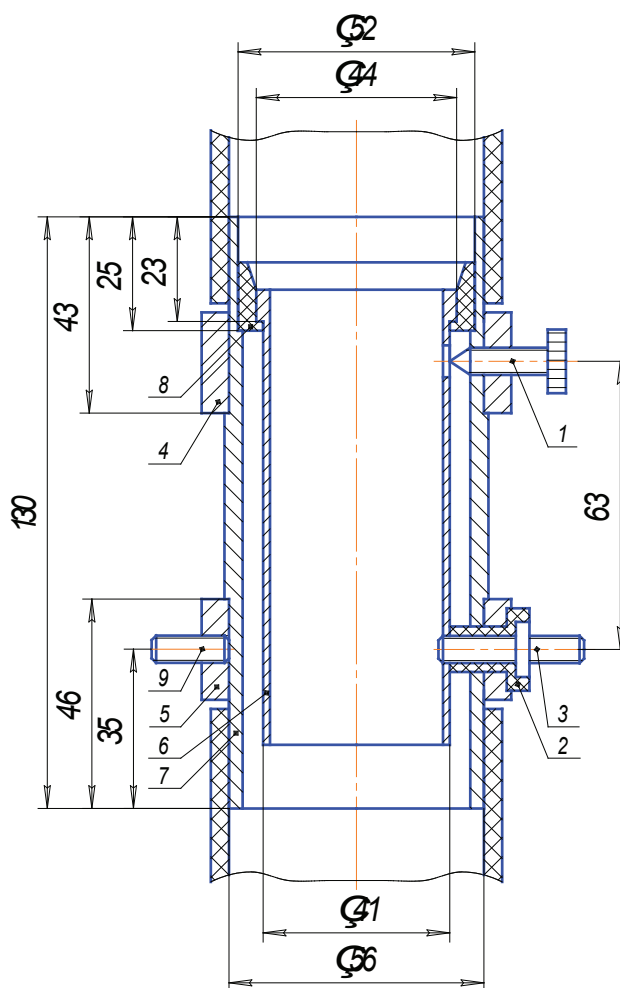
Устройство для терморегулирования рабочей жидкости: 1 — винт регулировочный; 2 — изолятор; 3 — клемма; 4 — кольцо верхнее; 5 — кольцо нижнее; 6 — корпус внутренний; 7 — корпус внешний; 8 — прокладка; 9 — шпилька клеммовая
